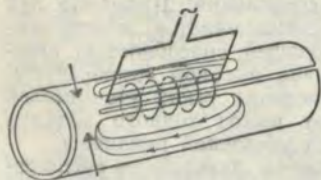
Схема индуктора для нагрева кромок полосы под сварку.
